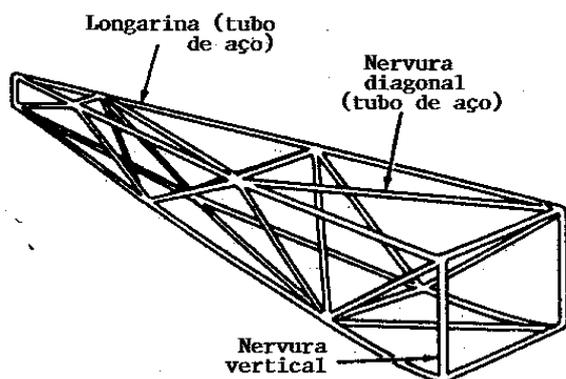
Estrutura de fuselagem tipo treliça, de tubos de aço soldados.
